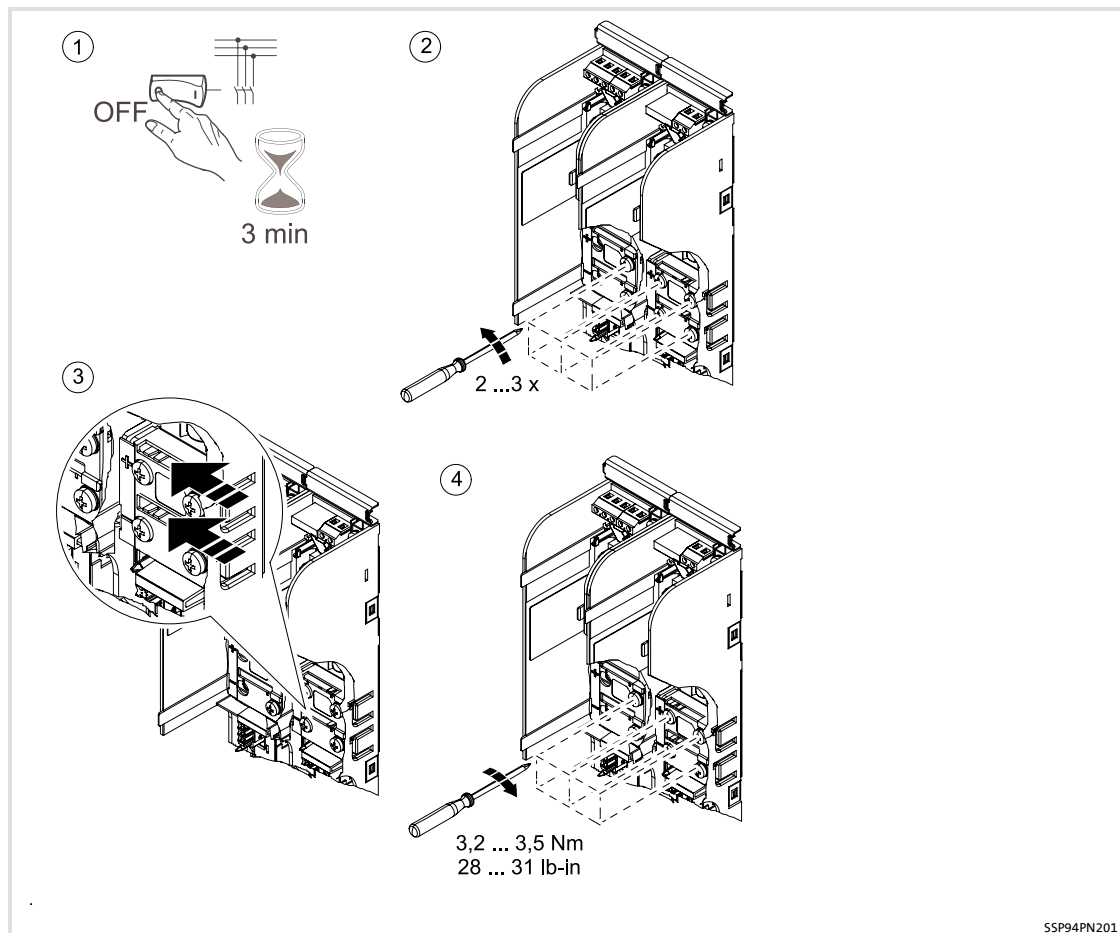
Esempio: collegamento delle sbarre collettrici al modulo di alimentazione DC
